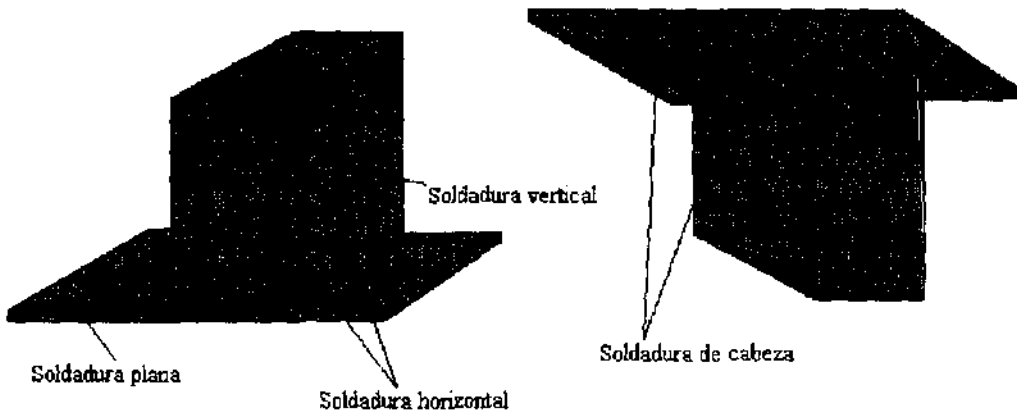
Soldaduras de acuerdo a la posición.
